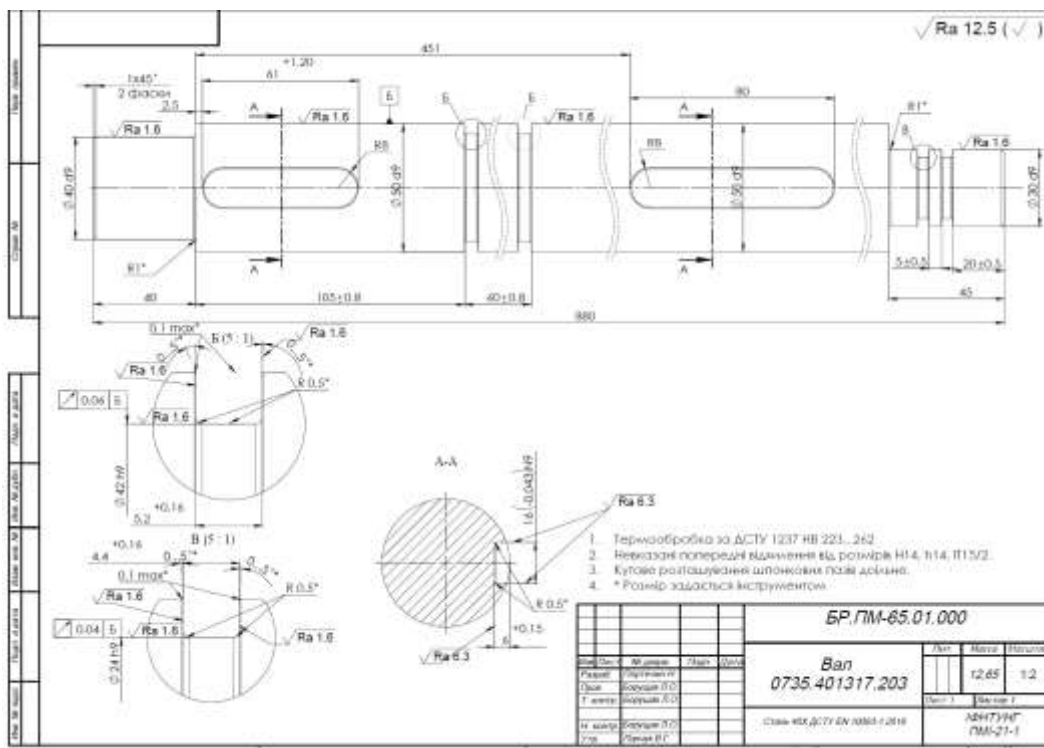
Креслення деталі «Вал 0735.401317.203»
